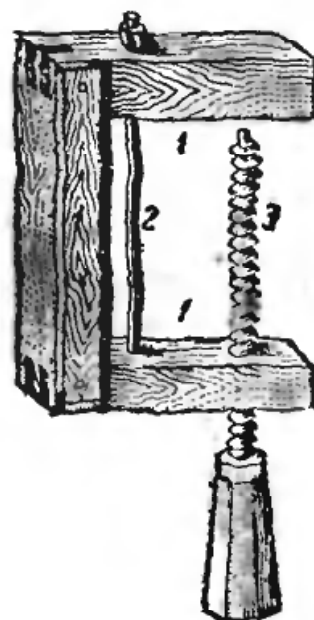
Струбцинка (деревянная): 1 — скоба; 2 — железный винт, стягивающий верхний и нижний бруски скобы; 3 — винт с рукояткой.
